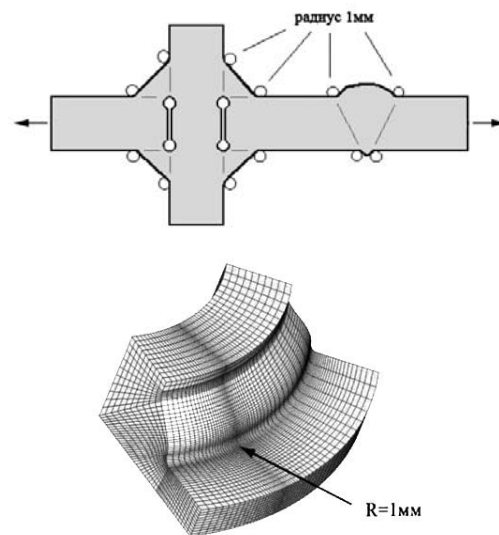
Эффективный концентратор напряжений в расчетной схеме сварного соединения
